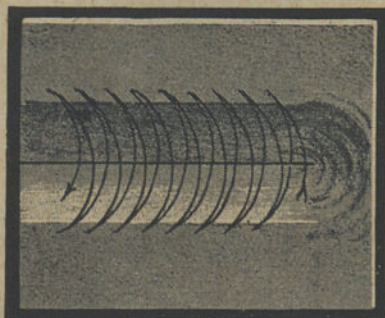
Movimentos do maçarico na soldadura de chapas grossas.
